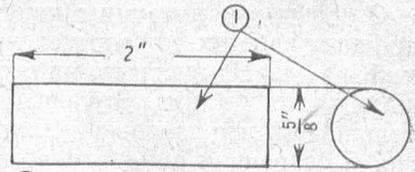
Образец из наплавленного металла для испытания на удельный вес. Обработать цилиндрическую и торцевые поверхности, размеры выдержать с точностью до  $1/1000$
